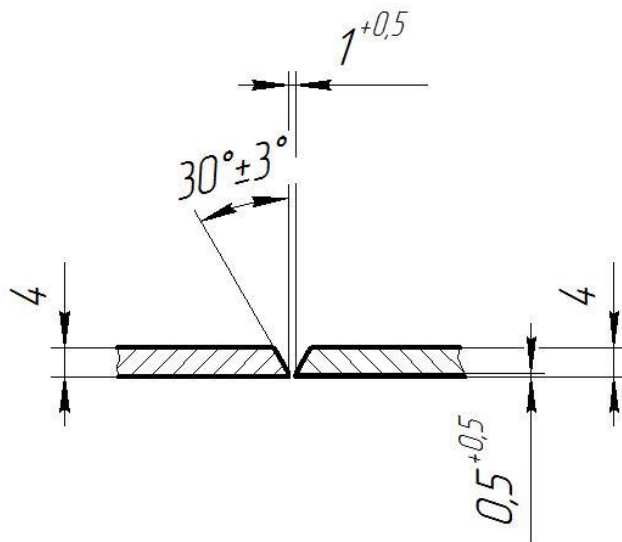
Кромки труб перед сваркой
